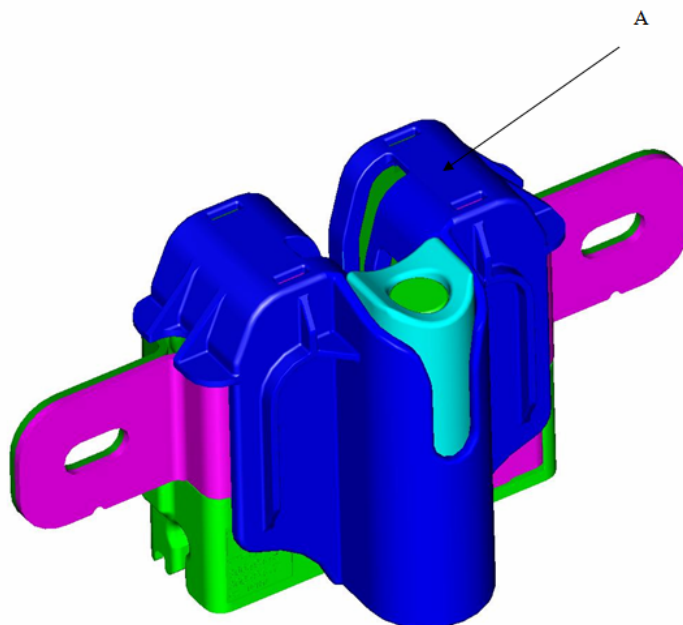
Schéma operace montáže 020 zámku typu Y283
